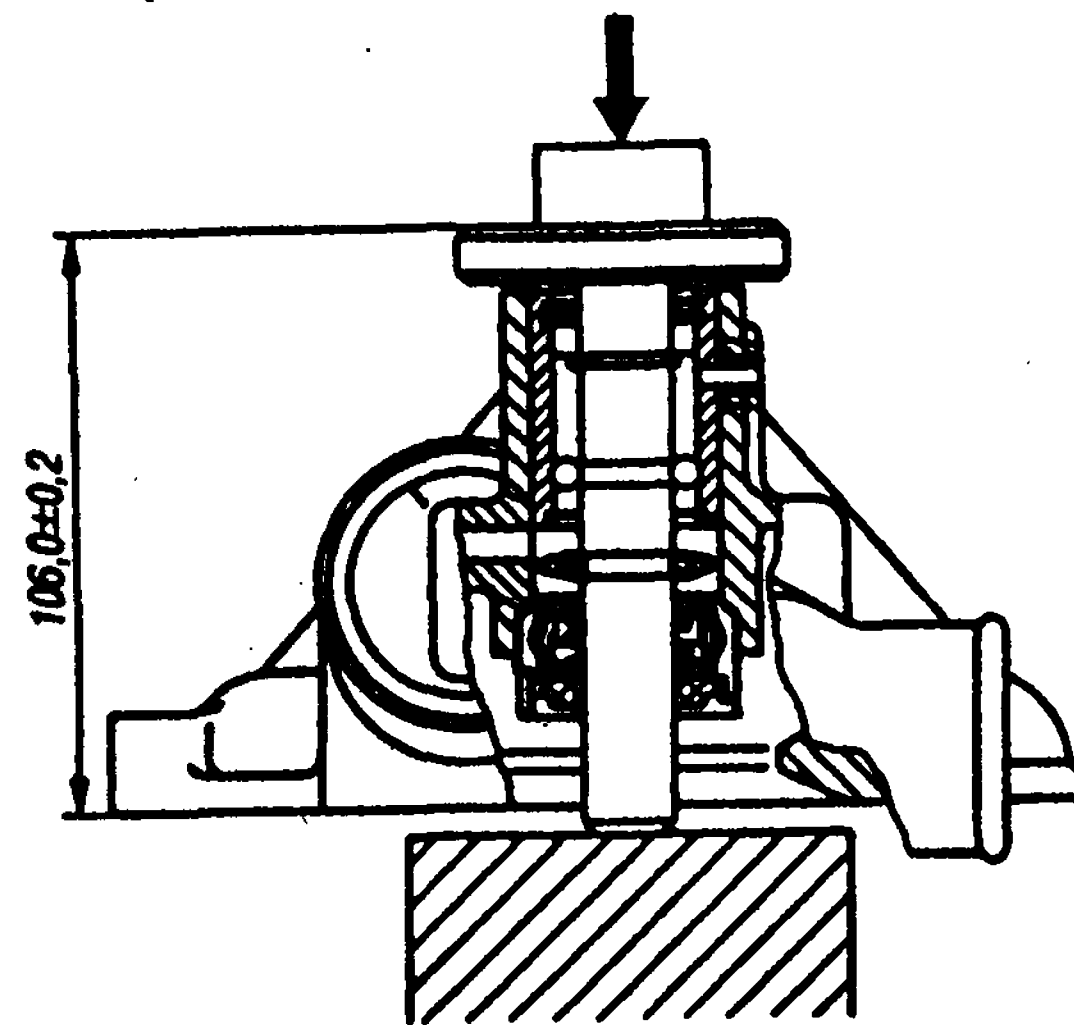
Напрессовка ступицы шкива водяного насоса на вал
